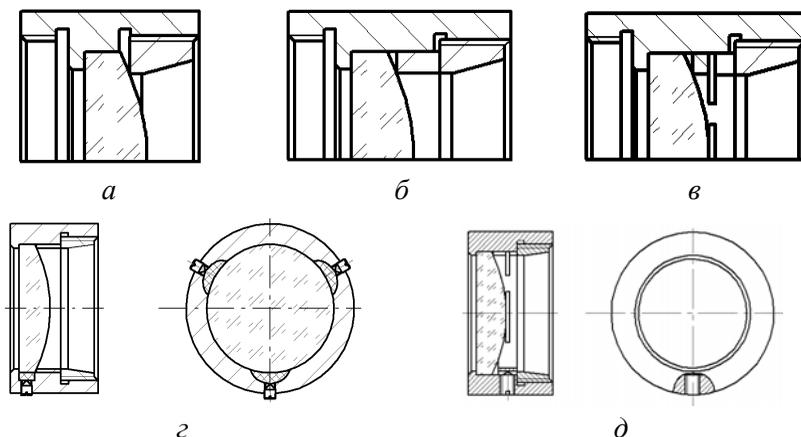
Крепление оптической детали резьбовым кольцом:
